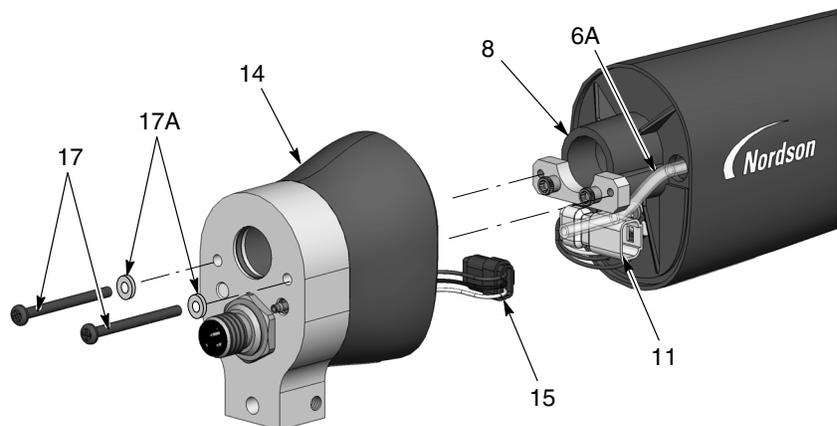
Desmontaje de la pistola de montaje en barra 1 de 3
